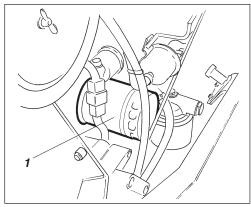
Motor Diesel (Isuzu) 1. Filtro de óleo
